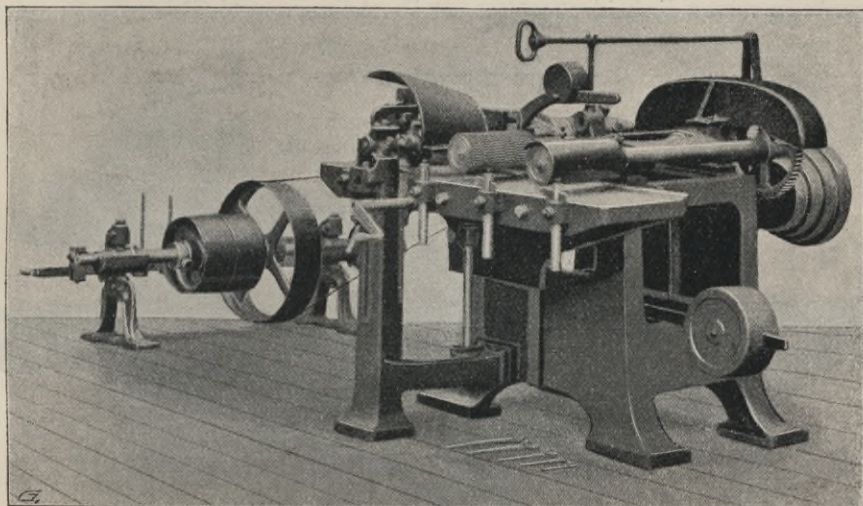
Kehlholmaschine mit einer Messerwelle.
